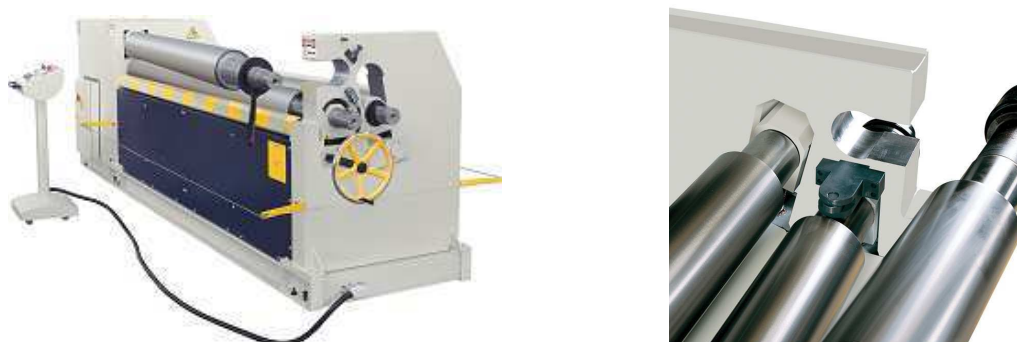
Motorové zakružovačky s ručně a motoricky ovládaným zadním válcem [10]
